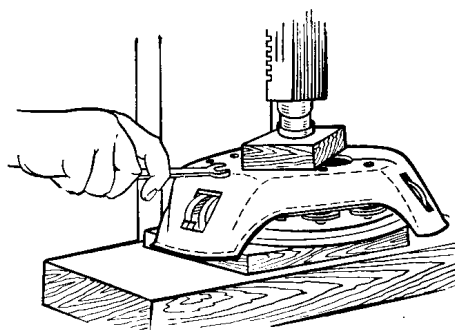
Установка на пресс нажимного диска с кожухом для разборки
